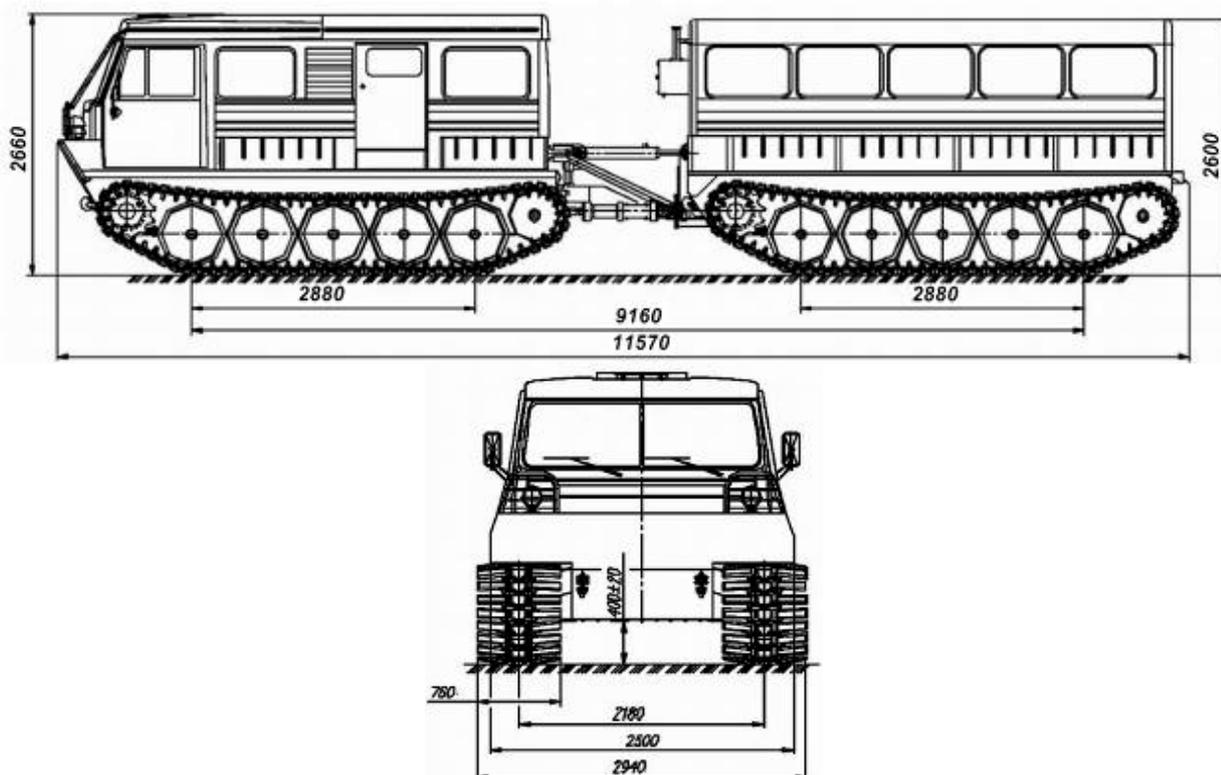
Габаритные размеры вездехода ТТМ-4901 ПС (Руслан)
